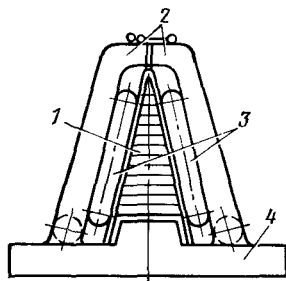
Схема приспособления для сборки хвостовых частей оперения с базированием по поверхности заполнителя:
